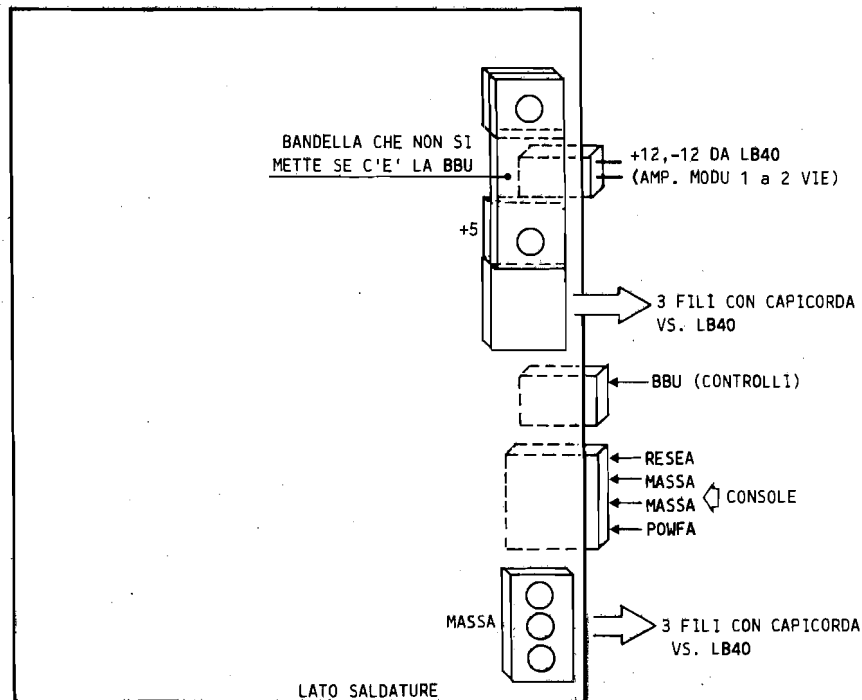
Vista posteriore del BACK PLANE e dei suoi connettori
